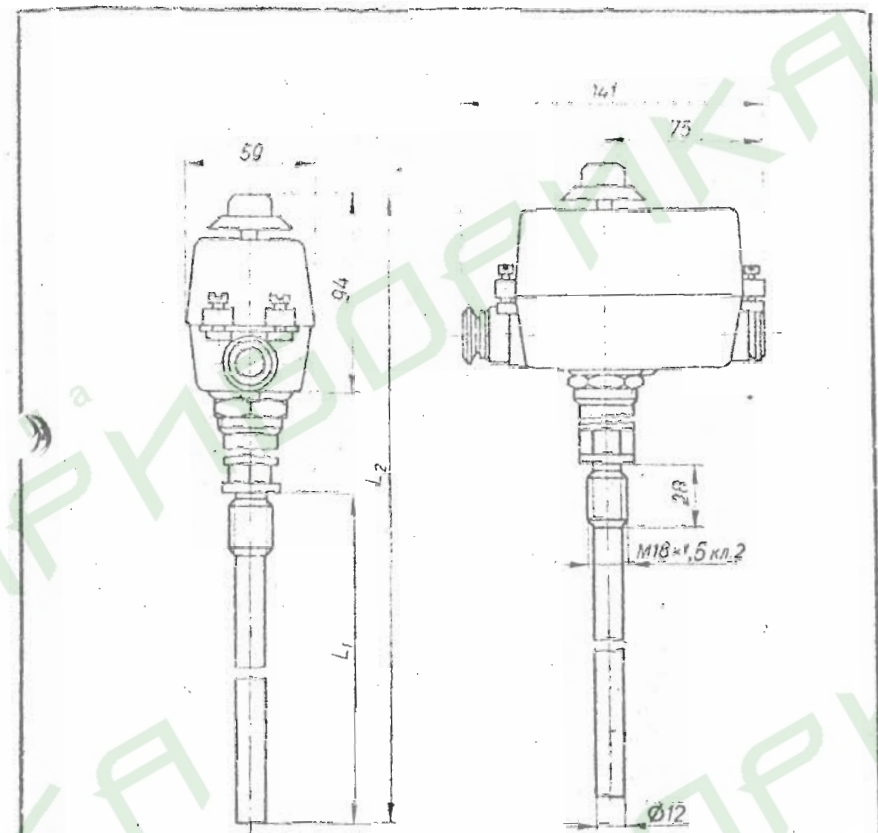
Габаритный чертеж ТУДЭ с замыкающими контактами
